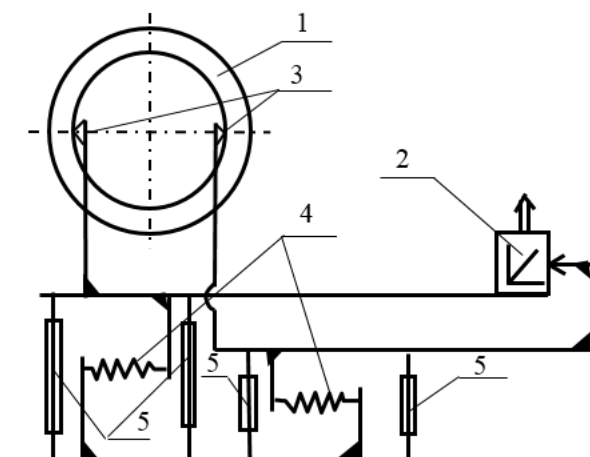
Вимірювальний пристрій для контролю внутрішнього діаметра деталі
